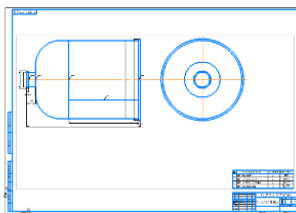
Чертеж сварной конструкции, выполненный в программе «КОМПАС 3D»
